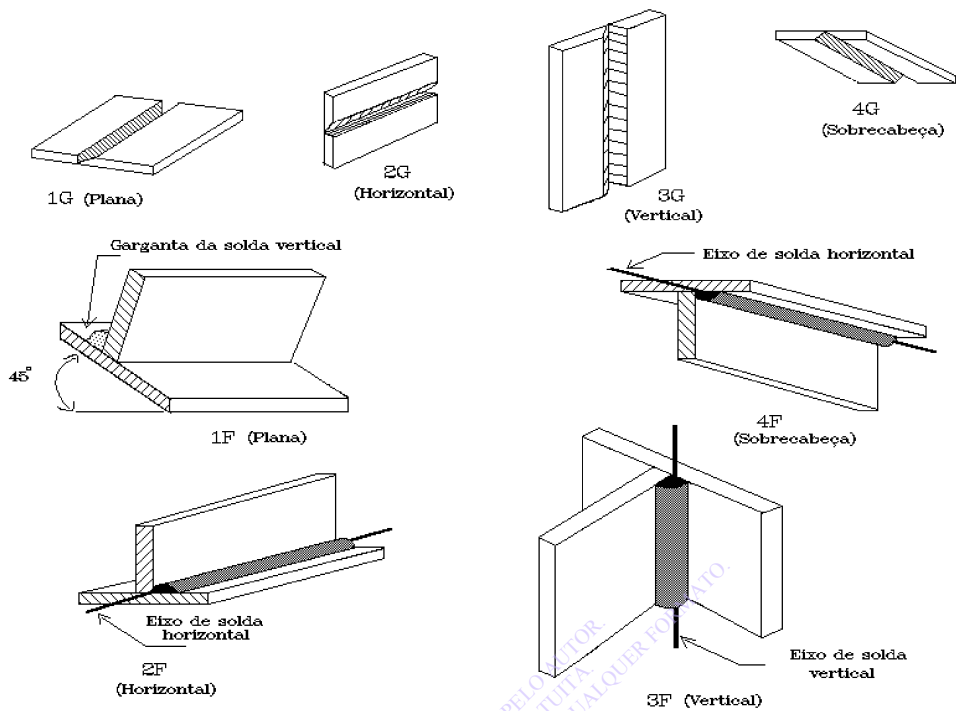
Posições de Soldagem Convencionadas pela ASME para Chapas.
